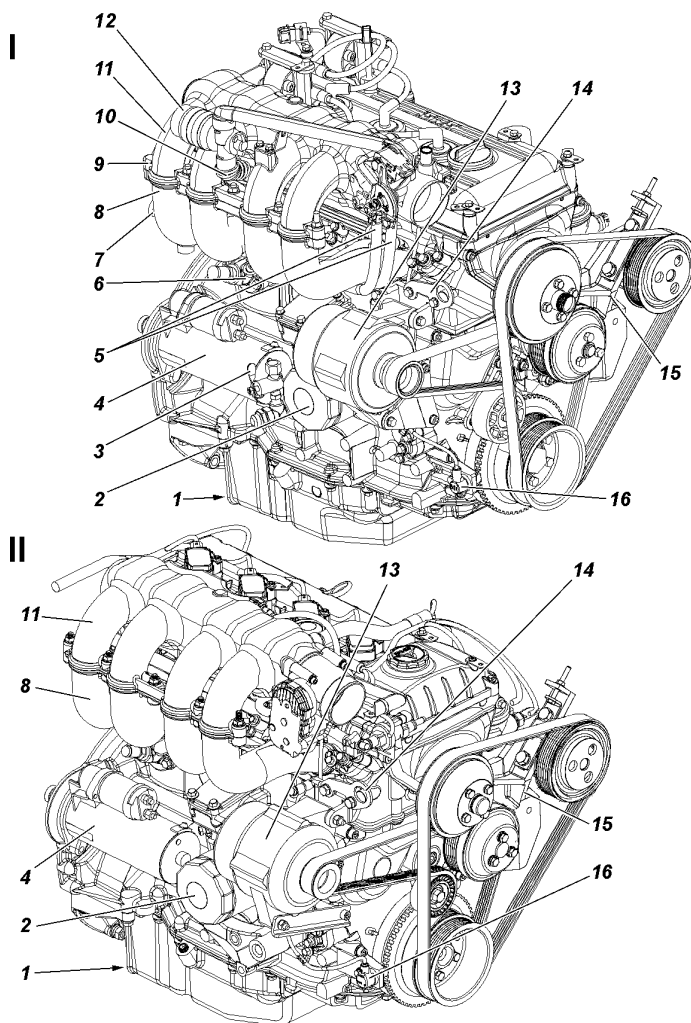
Двигатель ЗМЗ-409 (вид справа):
